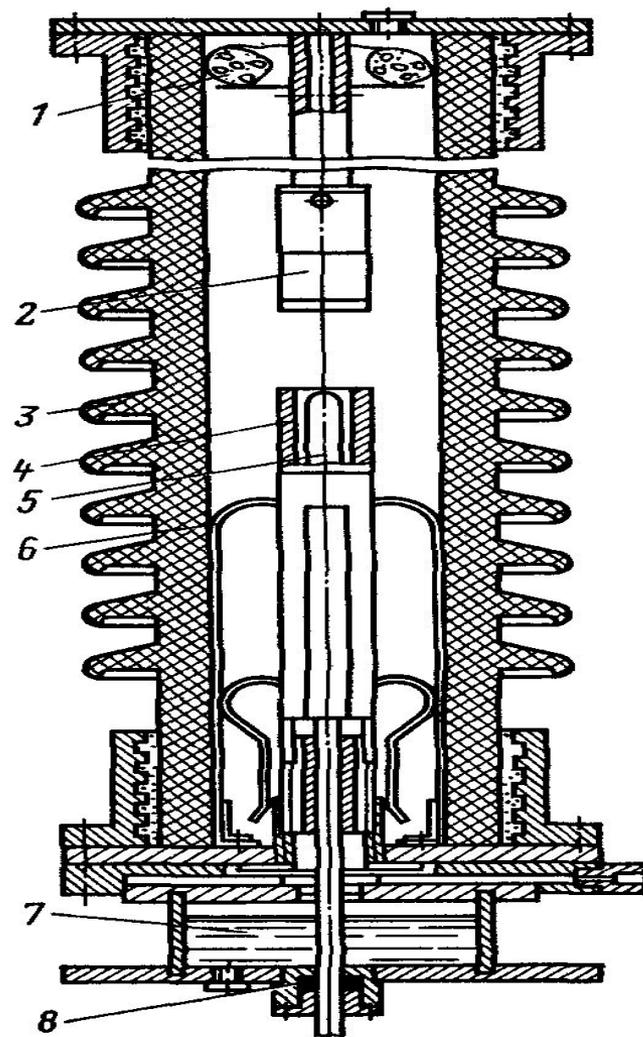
Контактная камера короткозамыкателя КЗ-110: 1 — мешочек с силикагелем; 2 — неподвижный контакт; 3 — фарфоровый корпус; 4 — экран; 5 — подвижный контакт; 6 — гибкая связь; 7 — масляный гидрозатвор; 8 — сальниковое уплотнение
